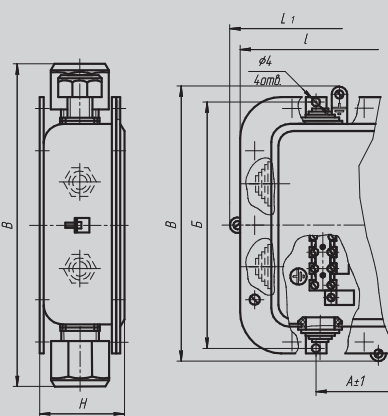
Коробки с втулками пластмассовыми уплотнительными
